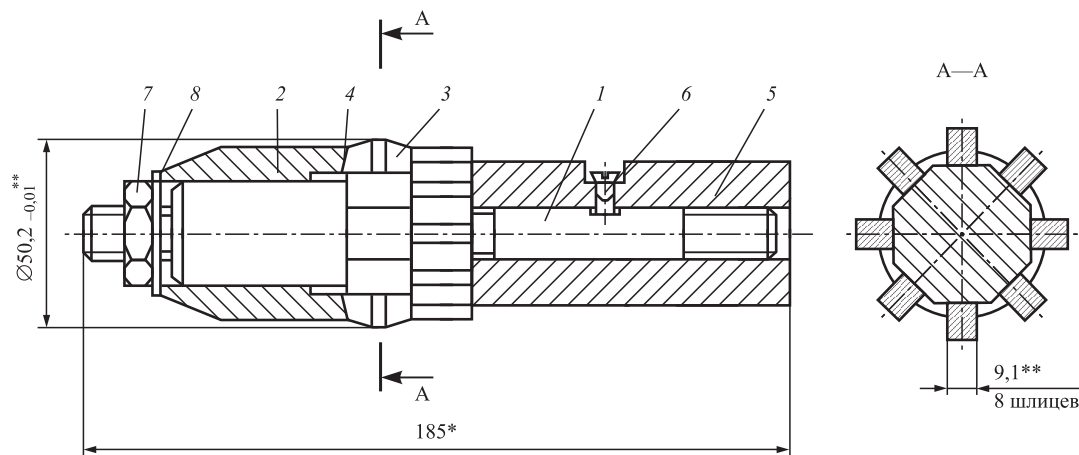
Прошивка для калибрования шлицевых отверстий:
